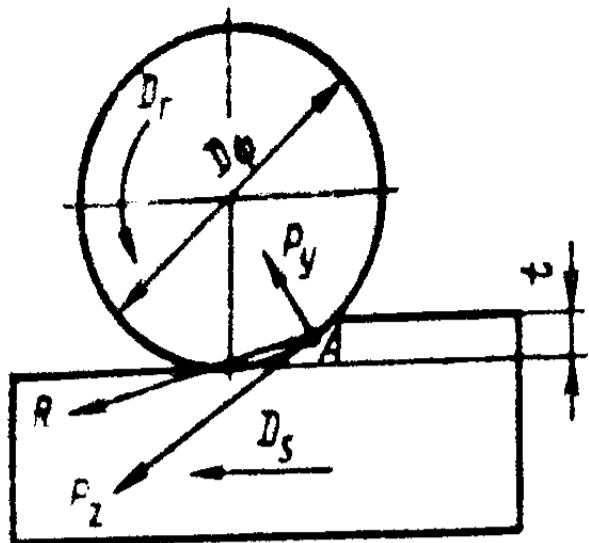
Силы резания при фрезеровании прямозубой цилиндрической фрезой
